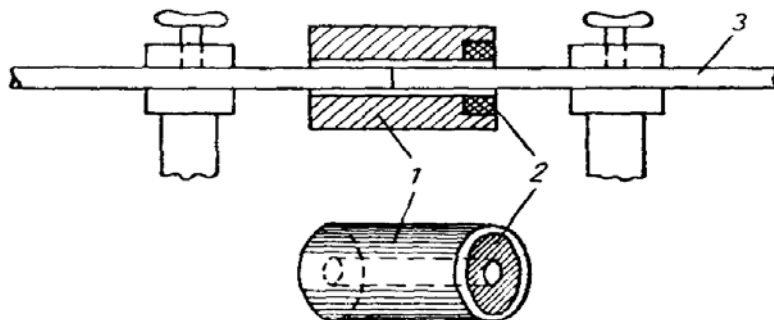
Термитная шашка для сварки проводов:
